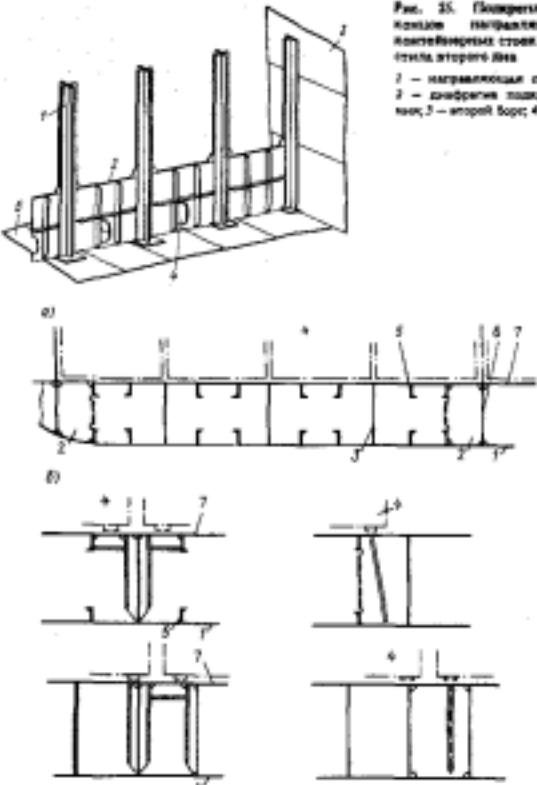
Подкрепление под углами контейнеров в двойном дне: а — поперечное сечение днища контейнеров; б — стойки и браши в двойном дне под углами контейнеров:
